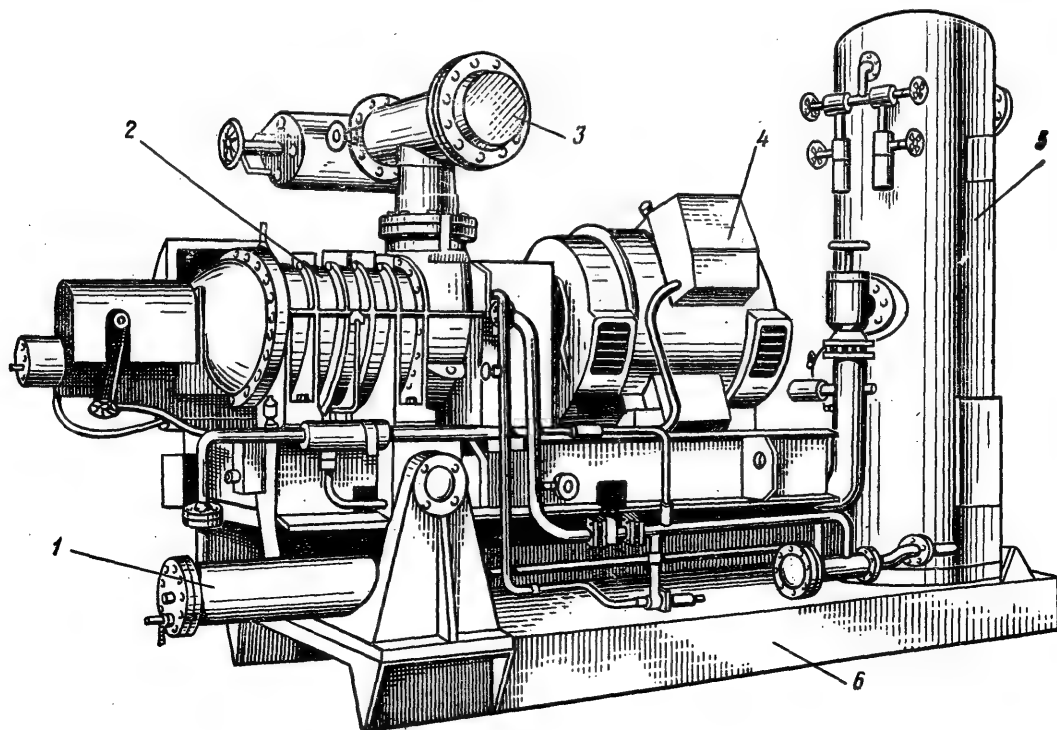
Винтовой холодильный компрессорный агрегат фирмы «Stal» (Швеция):
